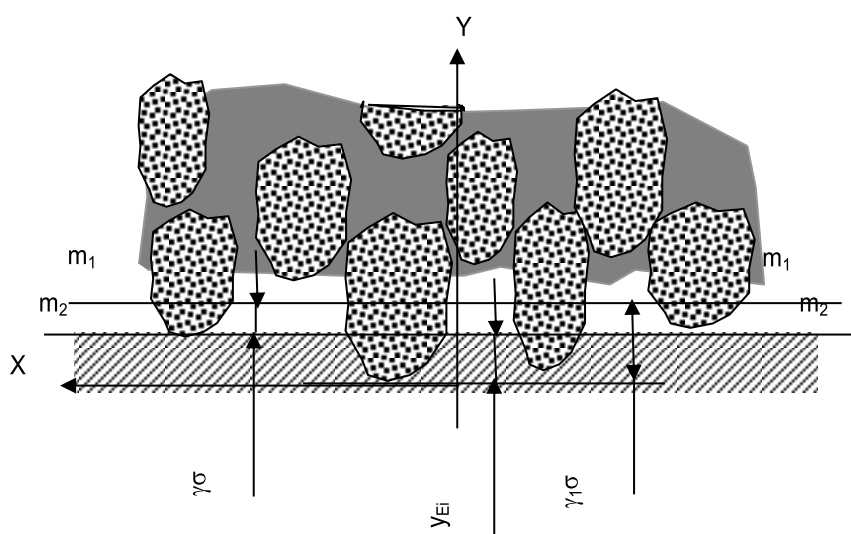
Схема взаимодействия эластичного круга с обрабатываемой деталью
